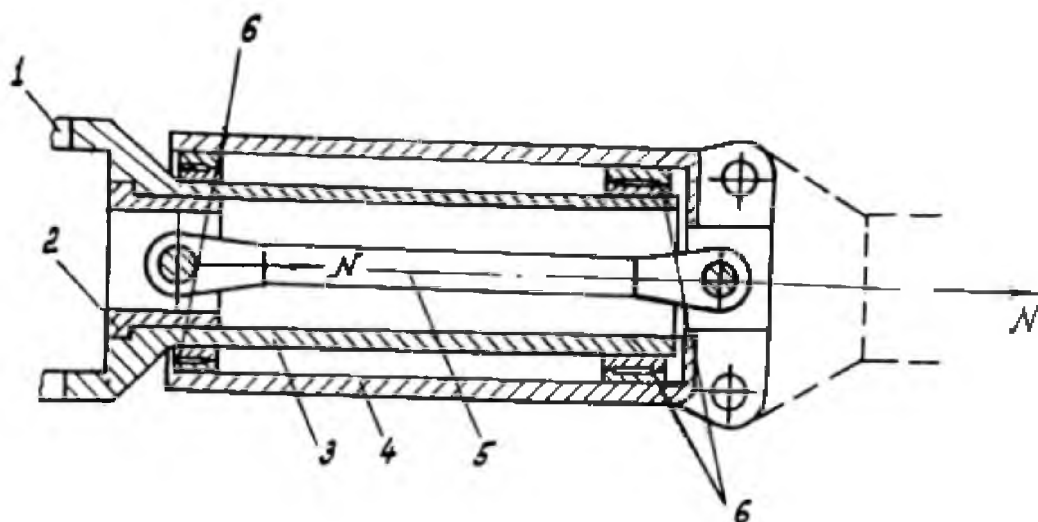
Схема нагружения осевого шарнира с проволочным торсионом втулки НВ тяжелого вертолета Ми-26 [23]: 1-проушина вертикального шарнира, 2-вкладыш, 3-цапфа, 4-корпус осевого шарнира, 5-проволочный торсион, 6-подшипники.
